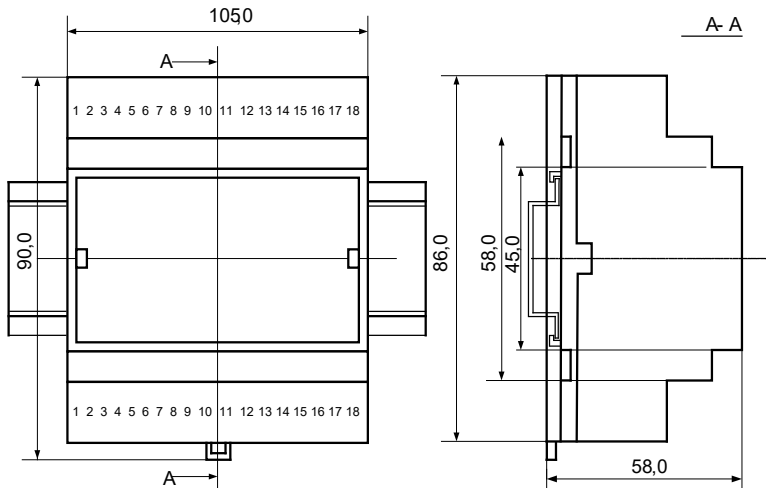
Габаритные и присоединительные размеры модуля
